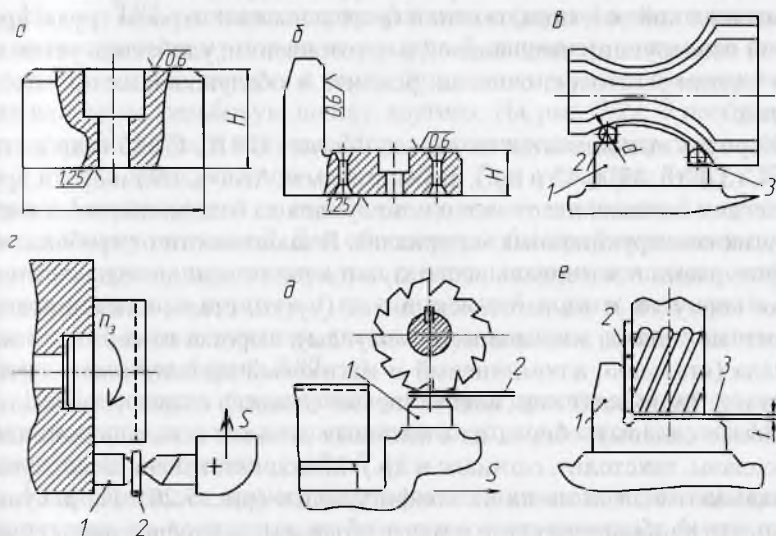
Высотный (*а*) и угловой (*б*) установы и примеры установки фасонной фрезы (*в*), резца (*г*), цилиндрической фрезы для периферийного фрезерования (*д*) и концевой фрезы (*е*) по различным установам с помощью шупов
